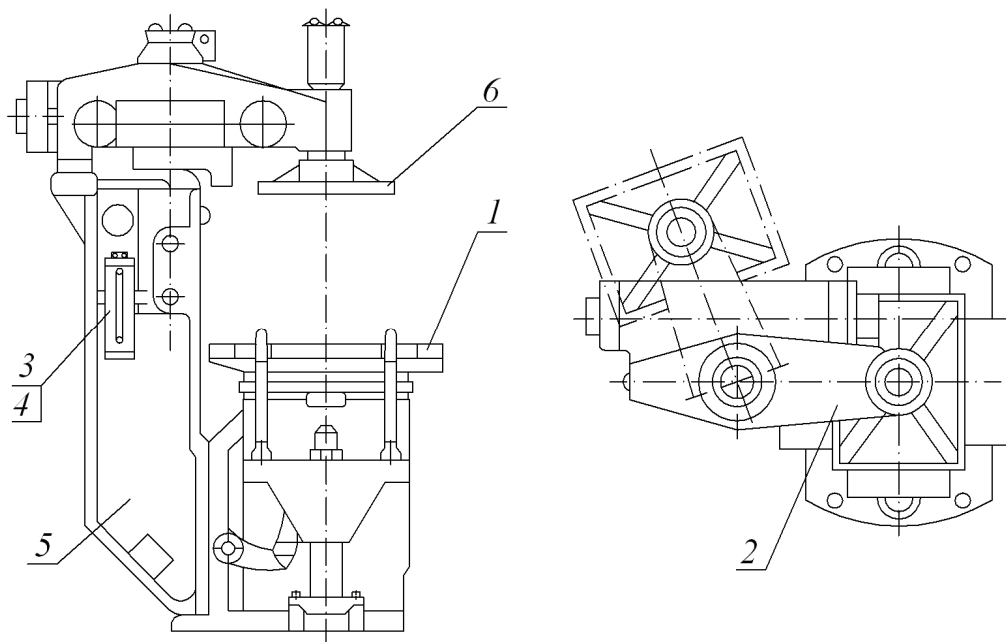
Устройство машины модели 4834: 1 – стол встряхивающий; 2 – траверса прессовая; 3 – бачок масляный; 4 – резервуар масляный; 5 – стойка; 6 – плита прессовая
